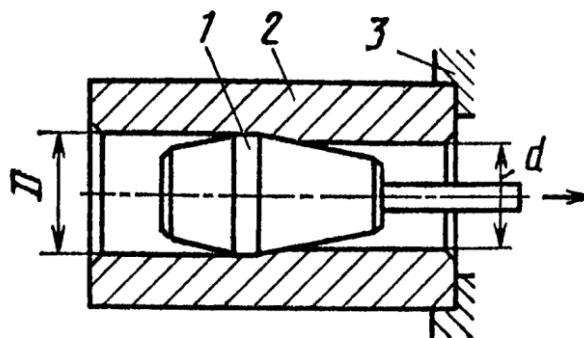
Обработка дорнованием 1 – дорн; 2 – обрабатываемая деталь; 3 – упорная плита станка
